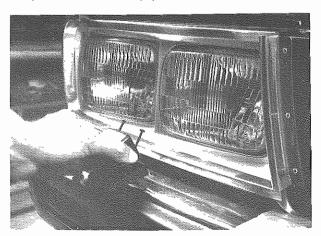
Smontare gli ugelli dei lavafari Disassembling headlight washer nozzles
